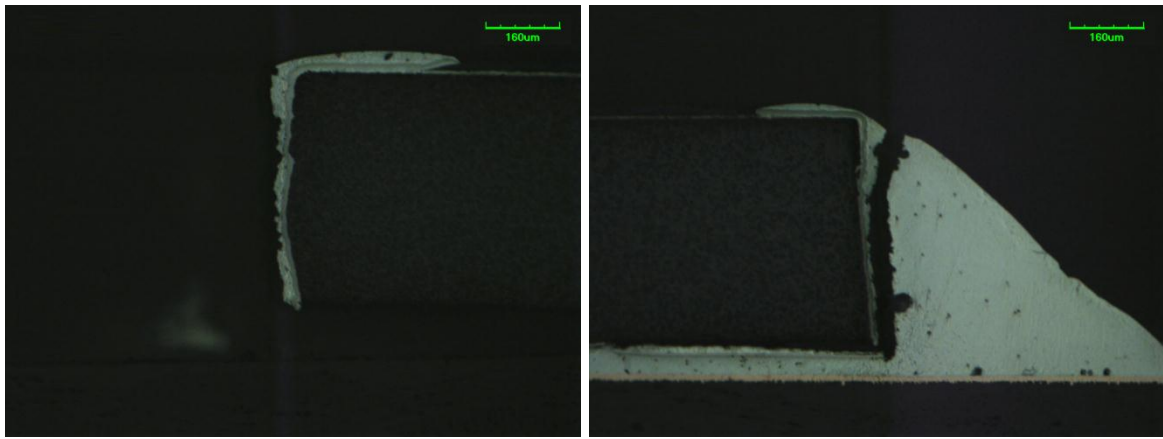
Řez pájeným spojem vzorku Cu-SAC-80-4-2-1 po odtržení součástky
